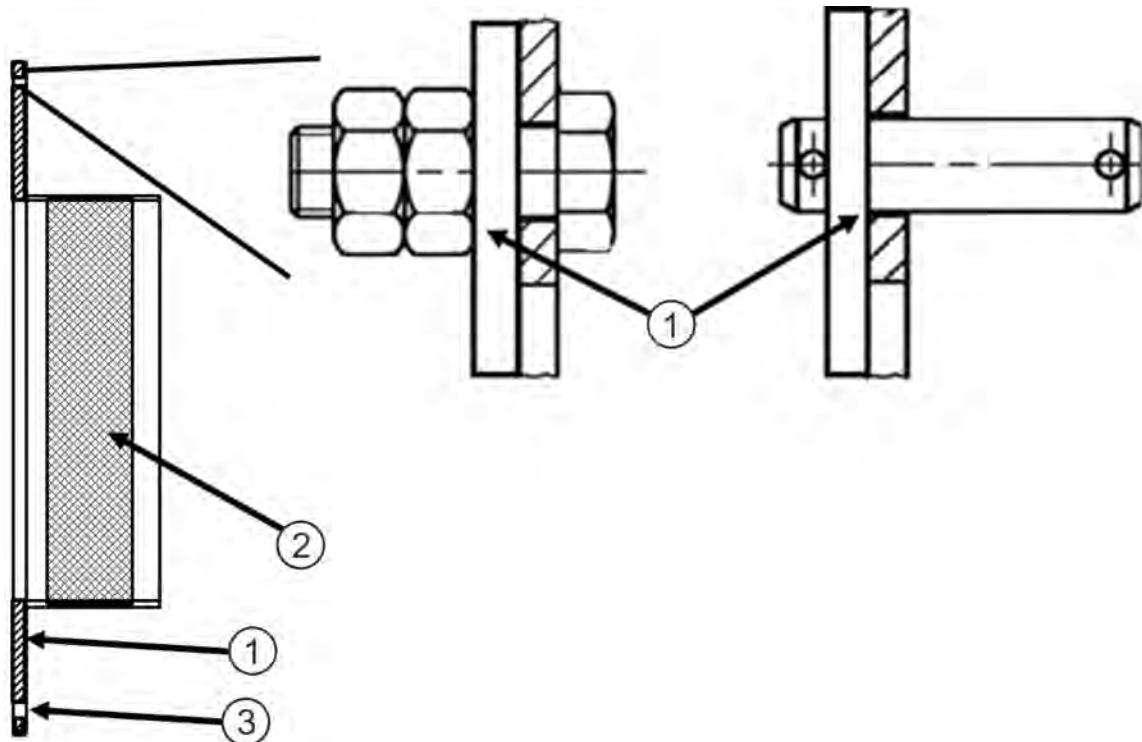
Katalysatormontage mit Doppelt gekonterter Gewindeschraube (links) und Splinten (rechts)
